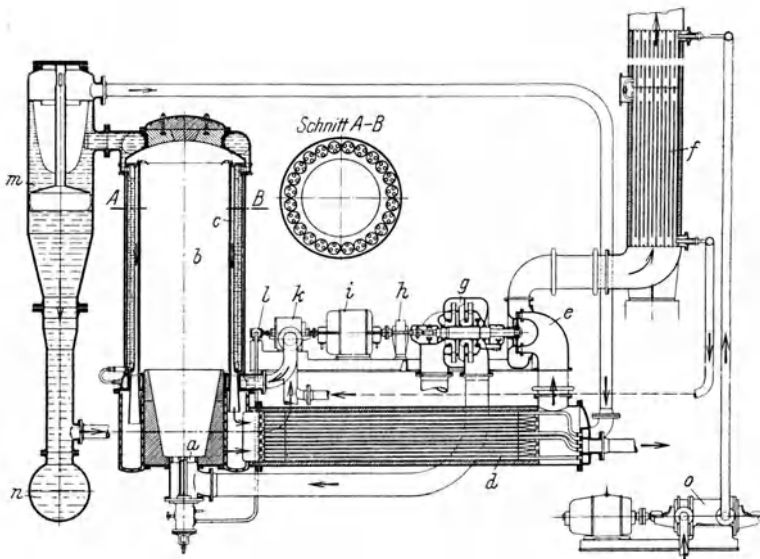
BBC-Velox-Gleichdruckkessel mit Abgasturbine und Kompressor für Ölverfeuerung.
